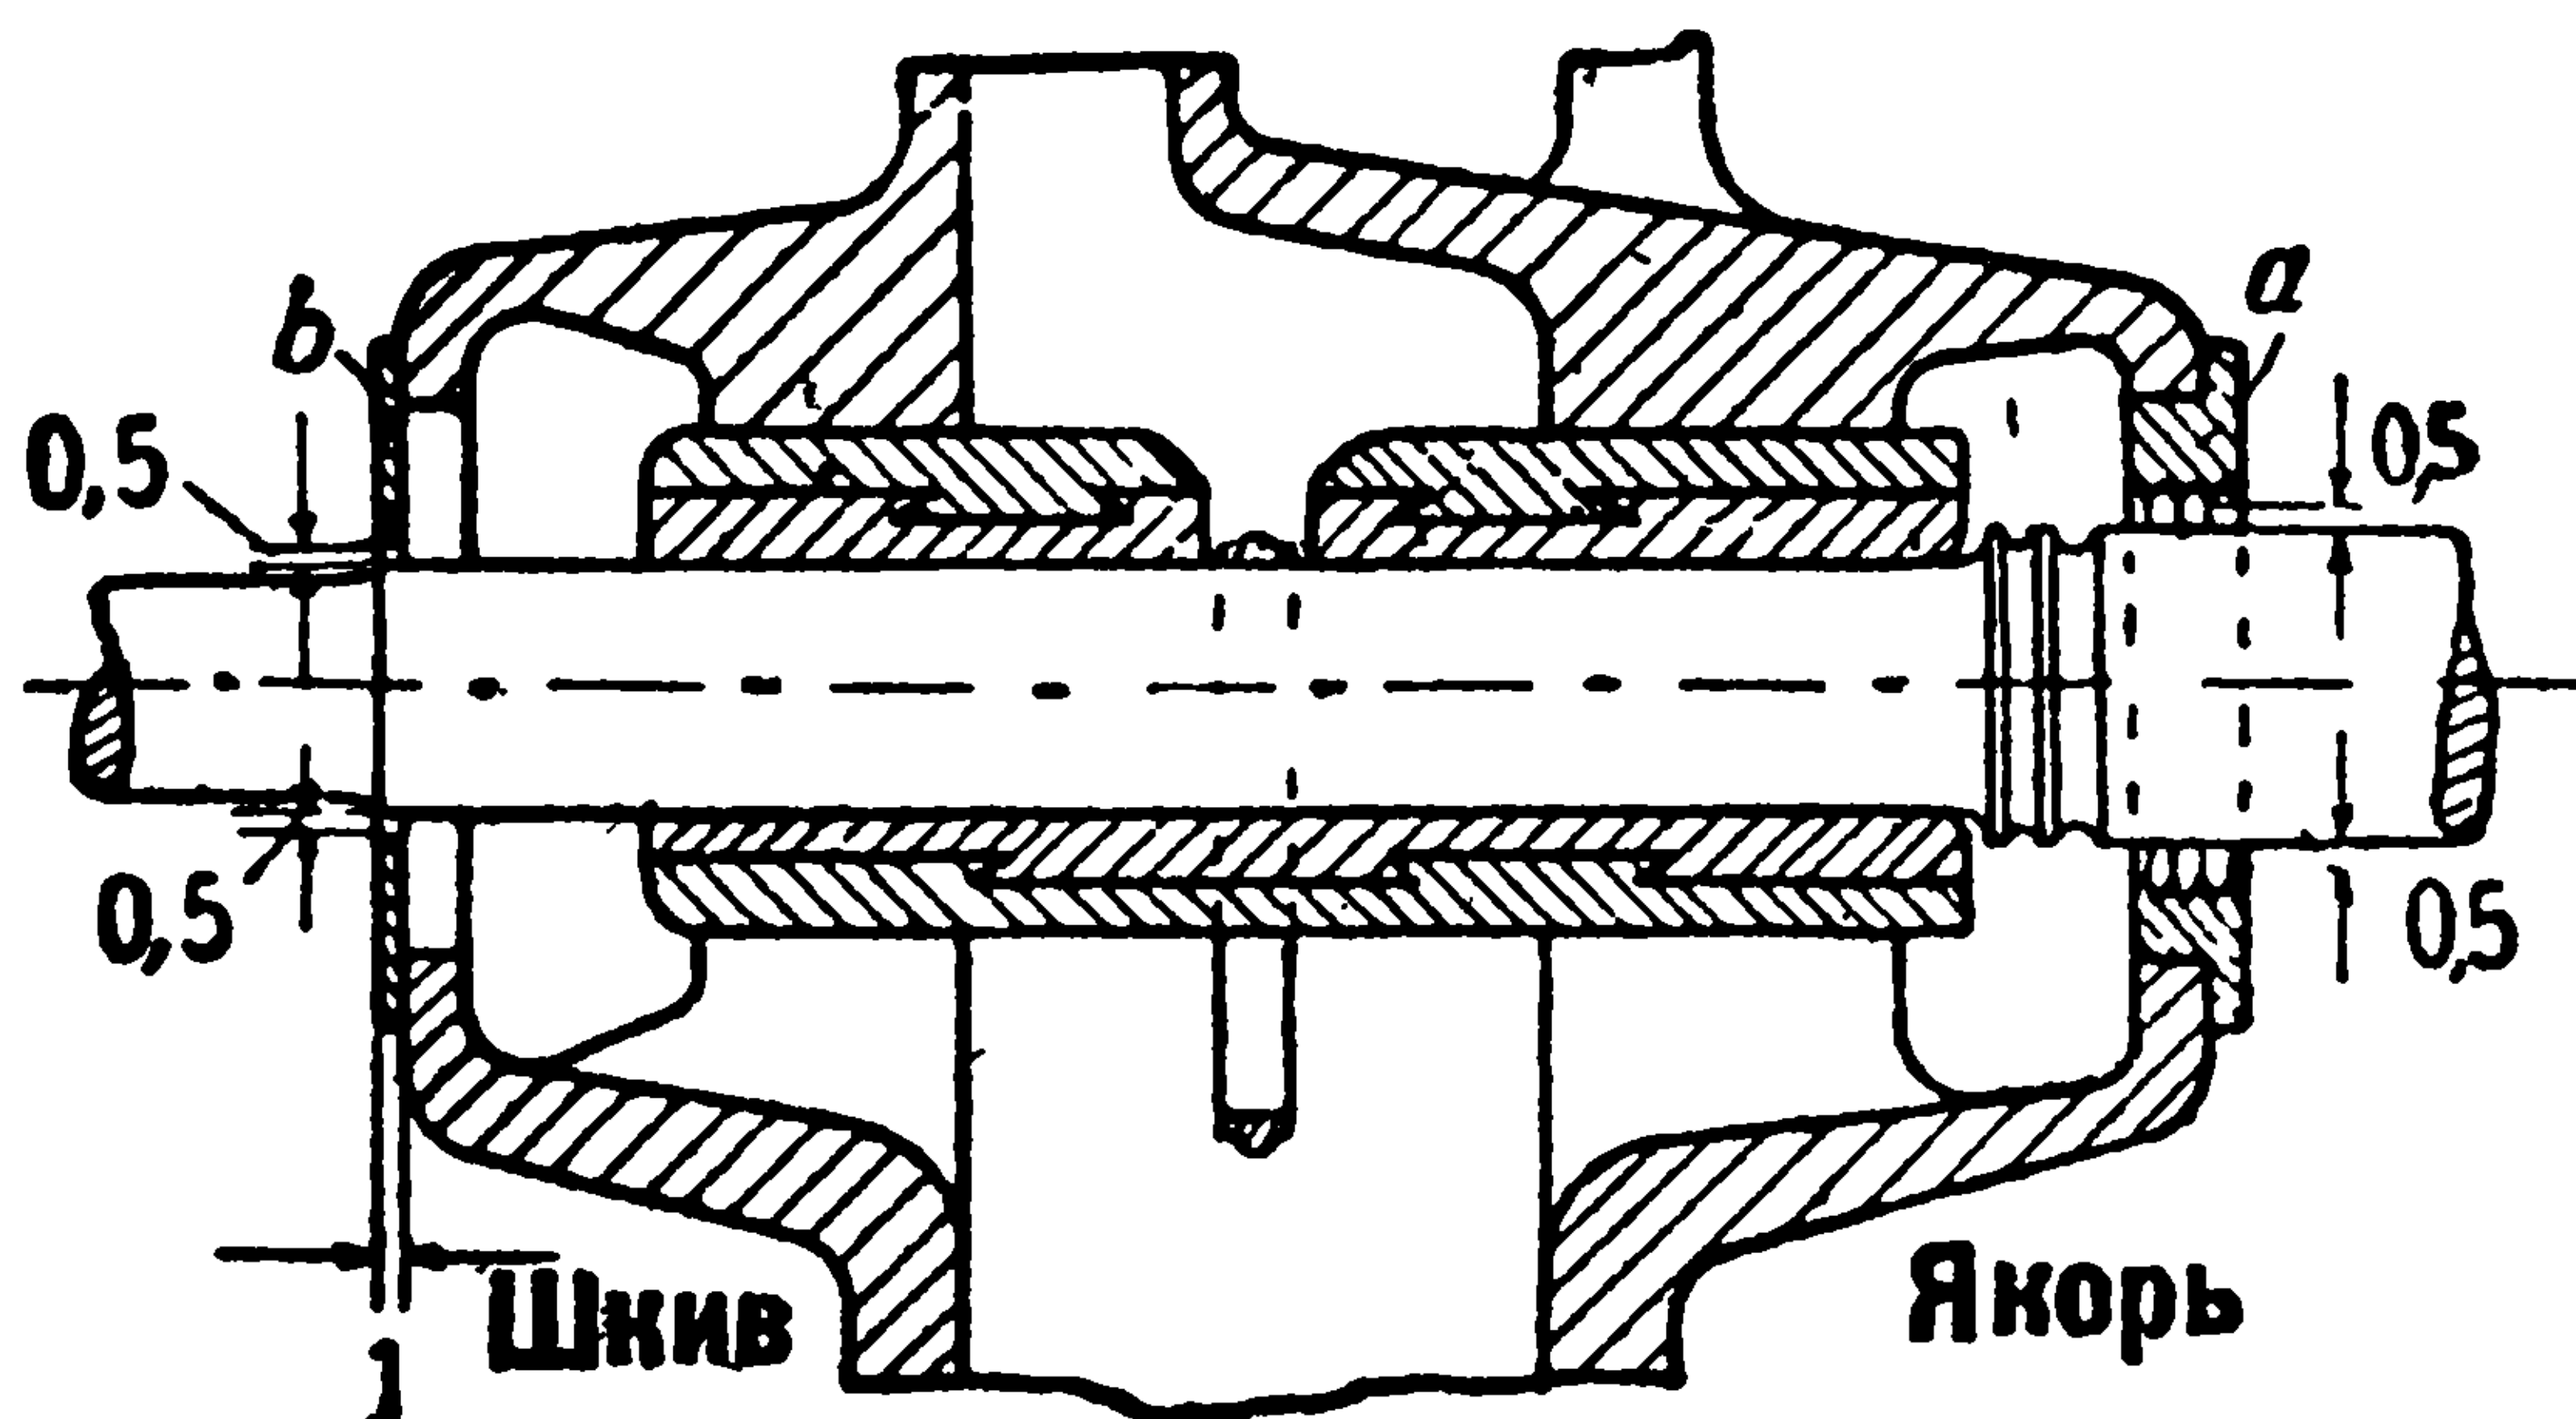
Уплотнительное кольцо и шайба на подшипнике.
